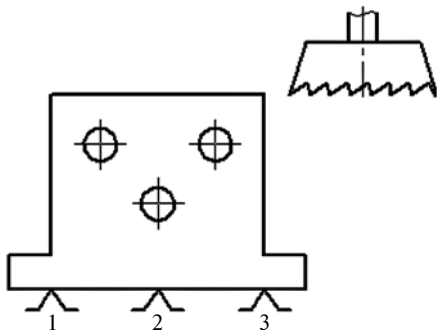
Схема обработки детали на вертикально-фрезерном станке
